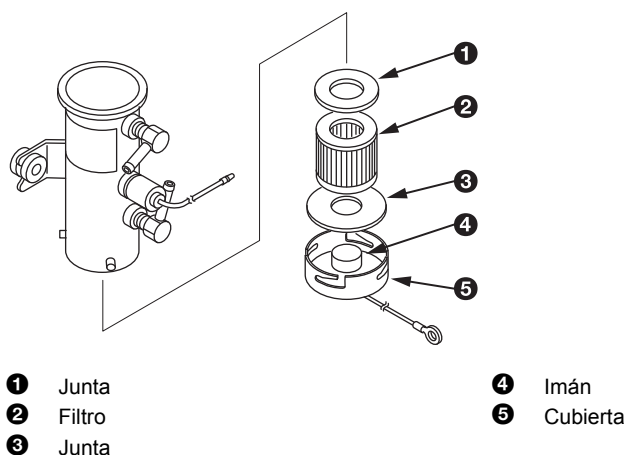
Filtro de la bomba de combustible de solenoide - Sustitución
